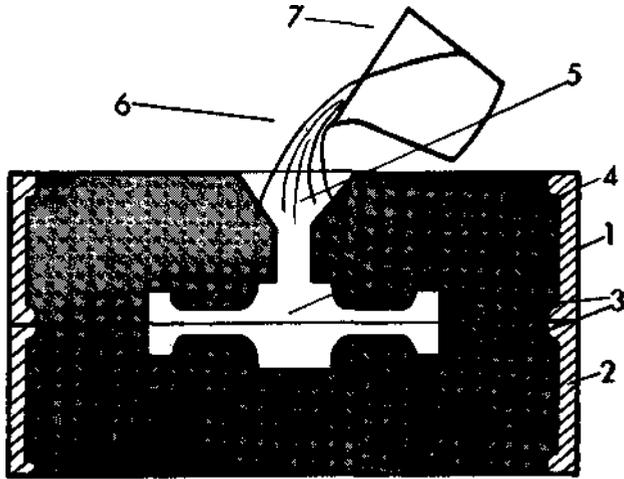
Sistema de moldear y fundir una rueda como la de la figura 8; 1, parte superior de la caja de moldeo; 2, parte inferior de la caja de moldeo; 3, arena de moldeo; 4, hueco dejado por el modelo de la pieza después de sacarlo; 5, agujero por donde se echa el hierro líquido; 6, hierro fundido líquido; 7, cazo para echar el hierro líquido.
